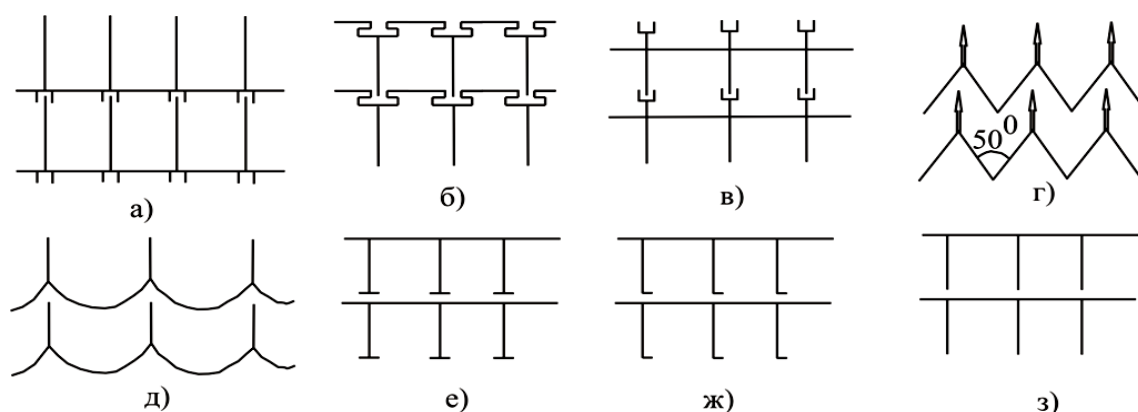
Различные варианты стыковки пластин в трубчатых блоках
